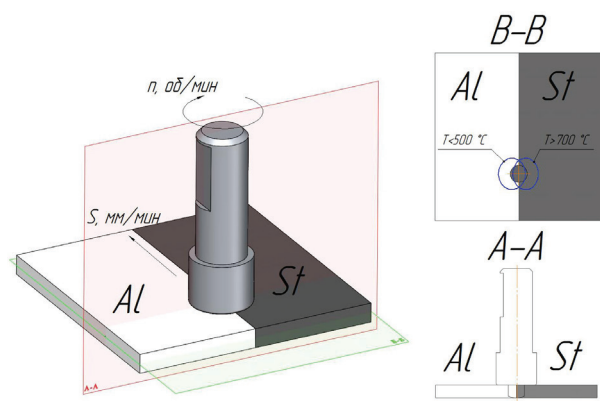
Стандартная схема сварки трением с перемешиванием применительно к сварке разнородных металлов
